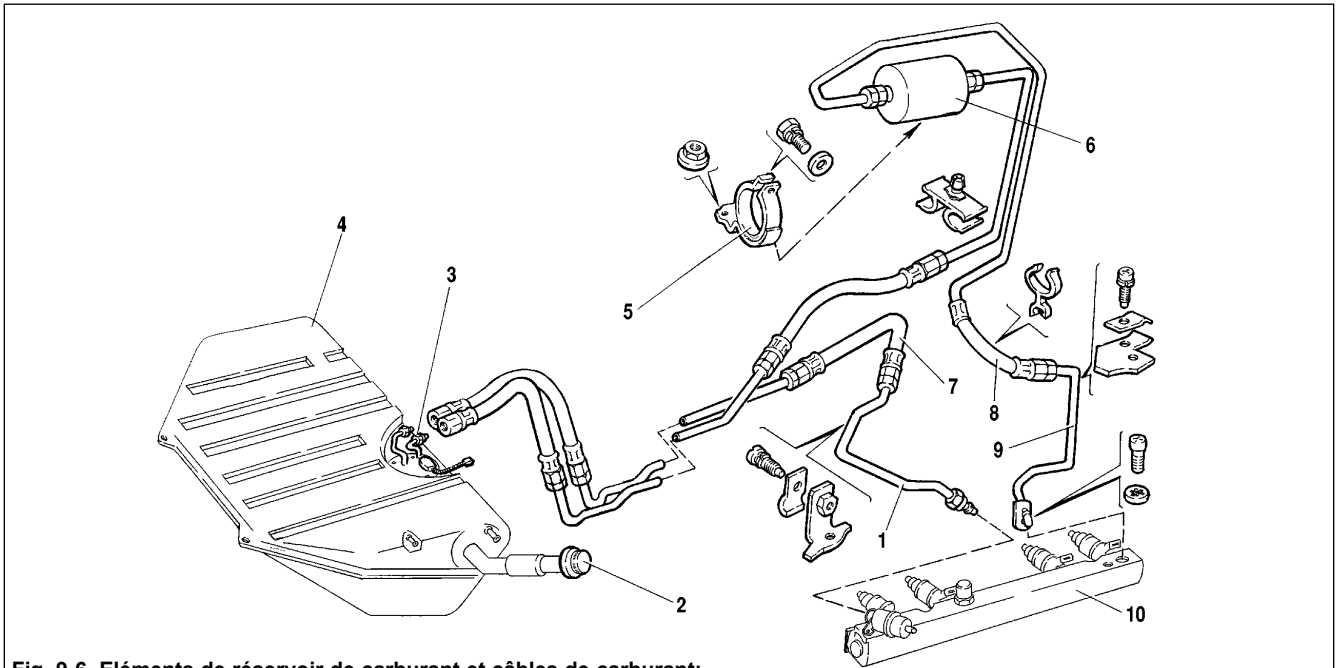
Eléments de réservoir de carburant et câbles de carburant:
